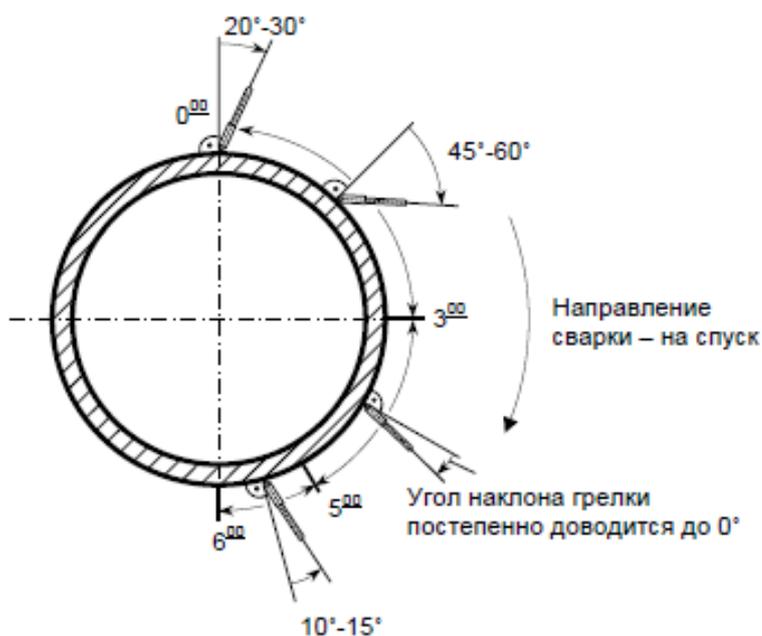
Изменение угла наклона сварочной горелки при механизированной сварке самозащитной порошковой проволокой неповоротных кольцевых стыковых соединений труб
